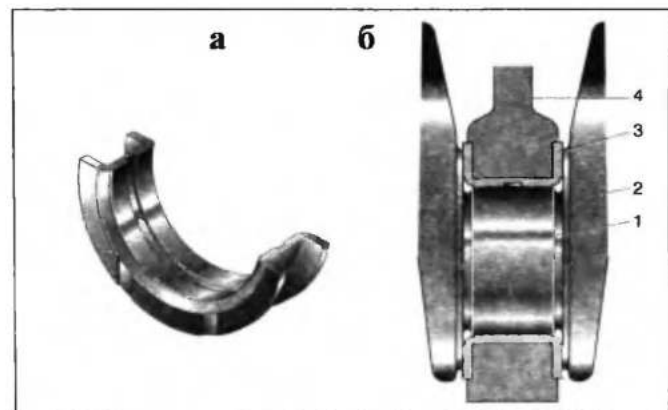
Фланцевый подшипник: а — вкладыш с упорными фланцами; б — установка пары фланцевых вкладышей; 1 — шейка вала; 2 — щека; 3 — вкладыш; 4 — опора
